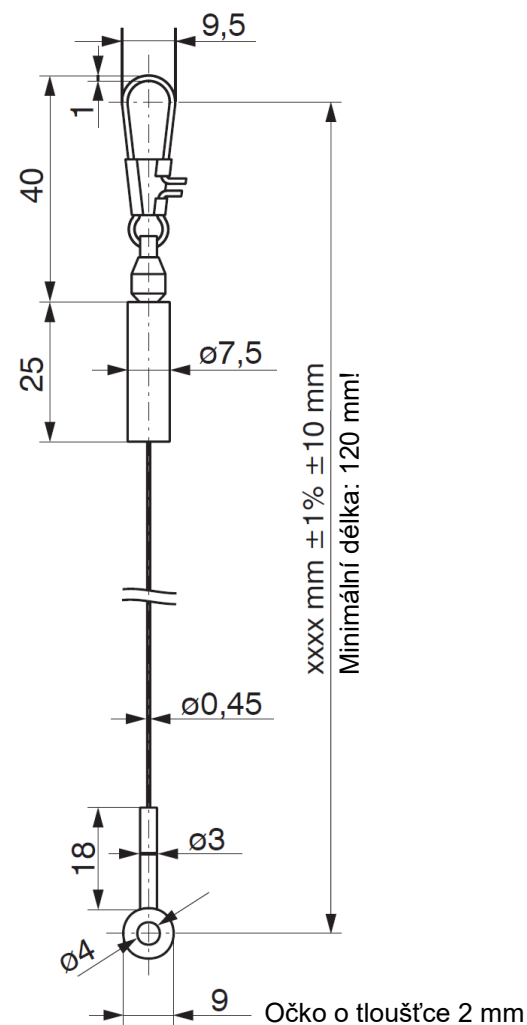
Montážní svorka MT60-WDS, rozměry jsou uvedeny v mm.
